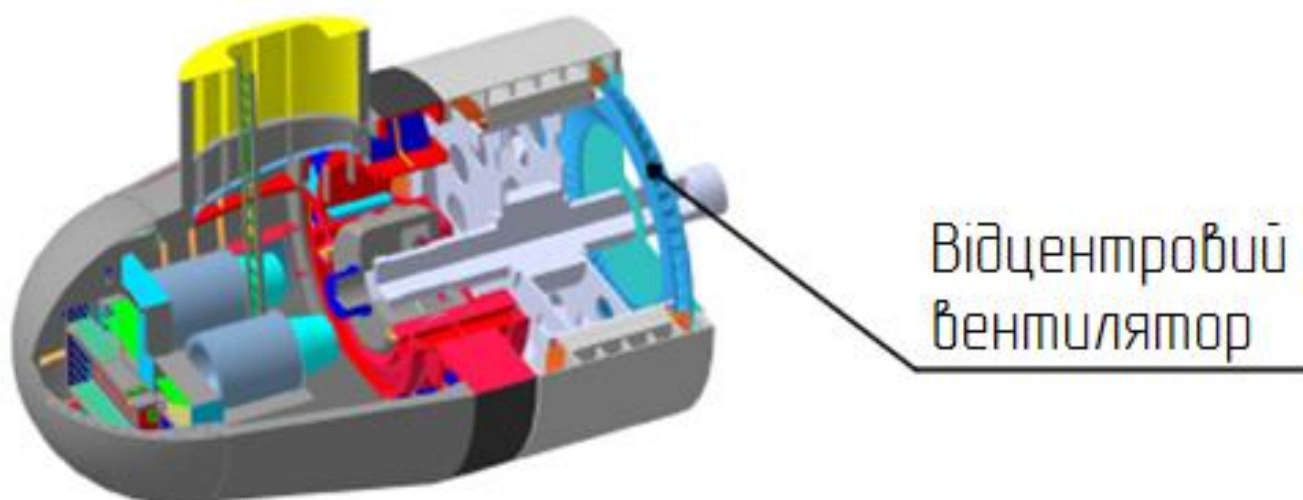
Загальна схема з допоміжним вентилятором
